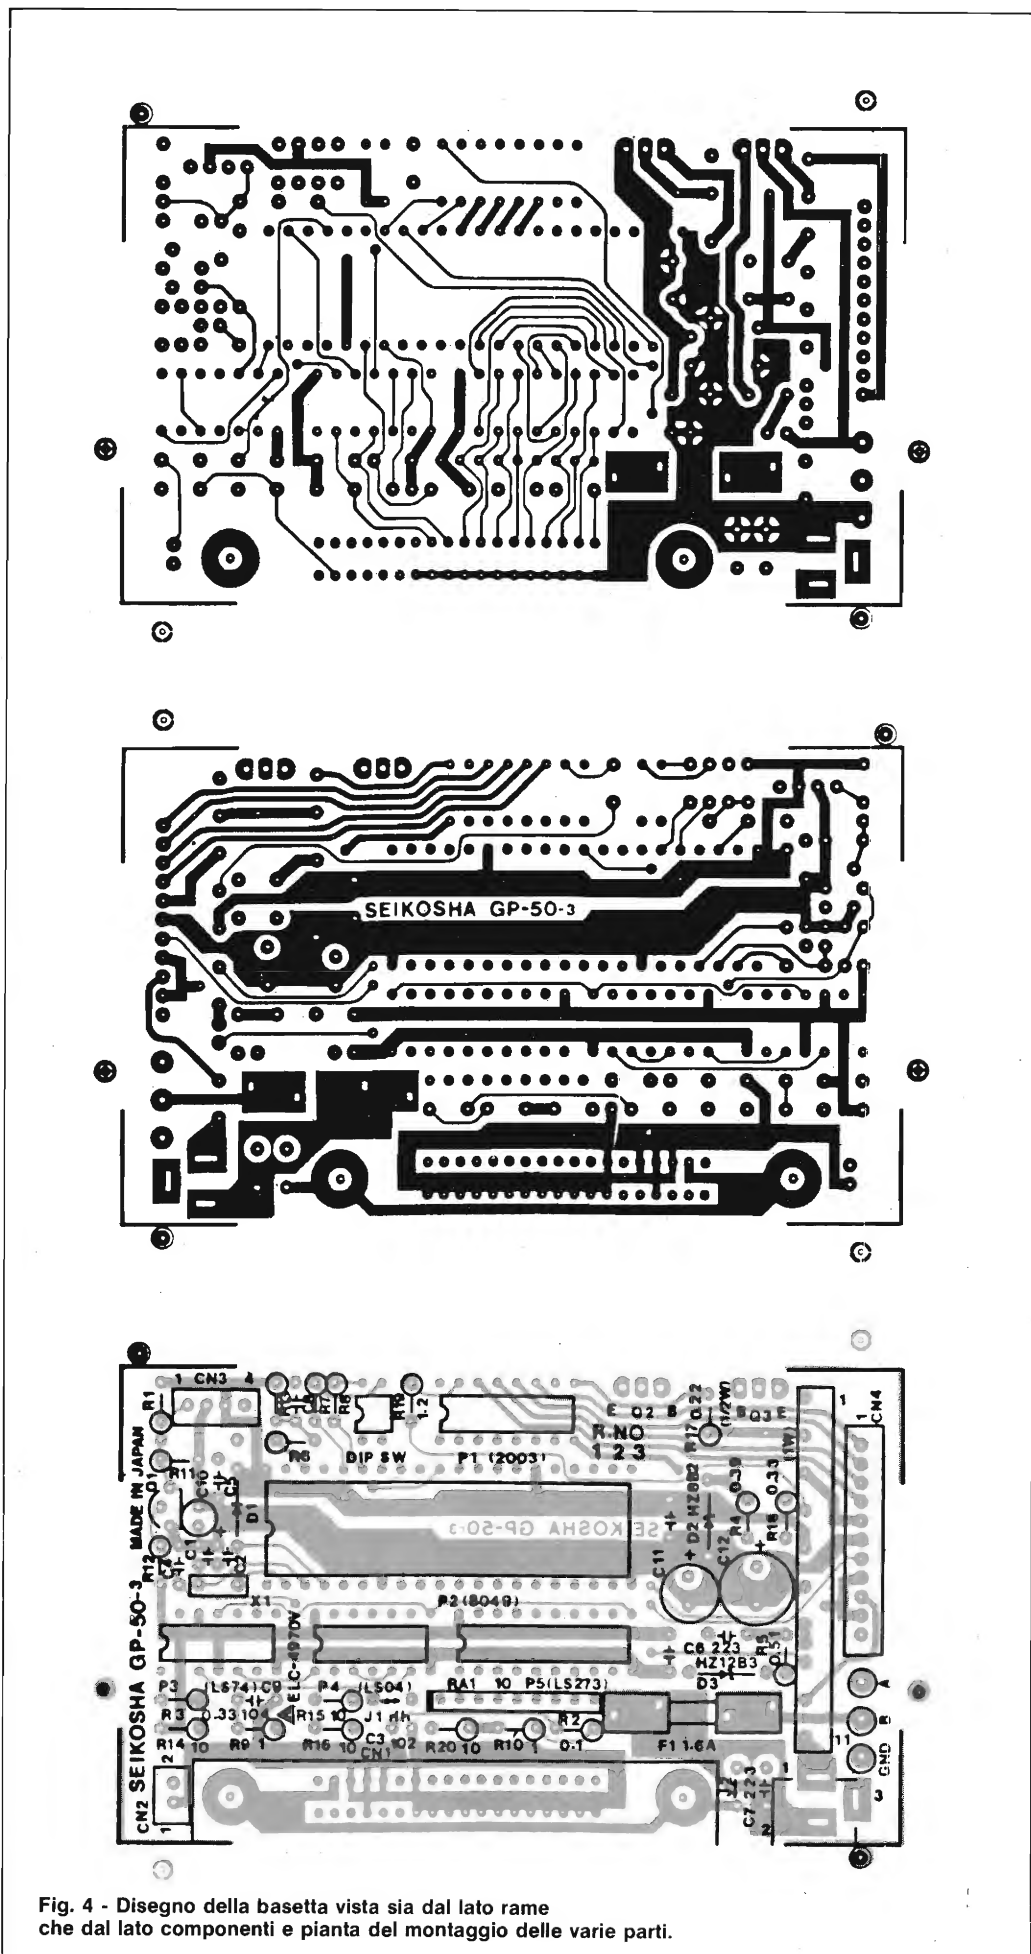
Disegno della basetta vista sia dal lato rame che dal lato componenti e pianta del montaggio delle varie parti.
